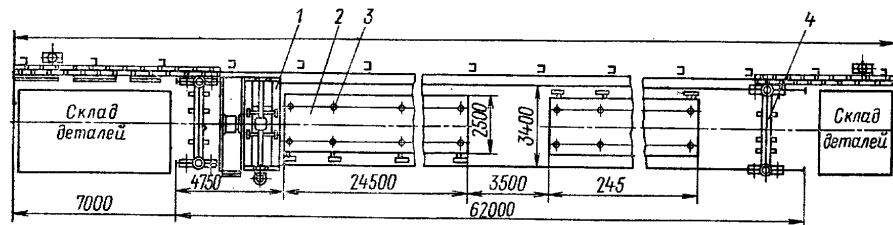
Стенд для сборки и сварки плоских узлов вагона
